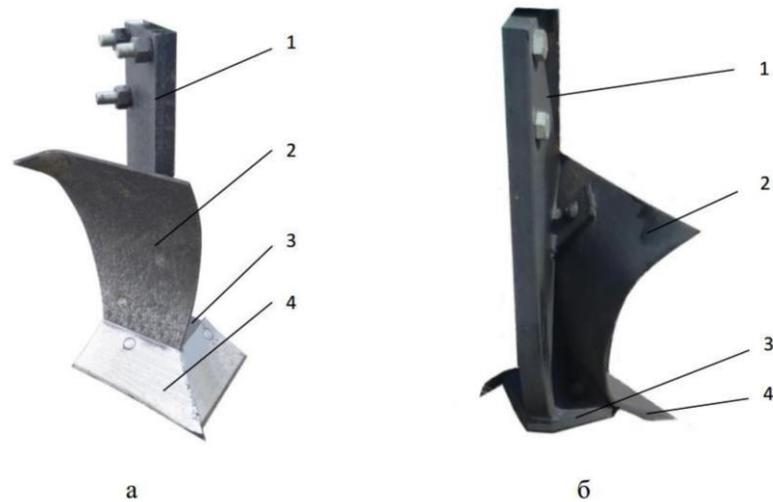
Модернізований корпус плуга СМІК-16-38: а – вигляд спереду; б – вигляд ззаду 1 – стійка; 2 – відвал; 3 – башмак; 4 – стрілочаста лапа
